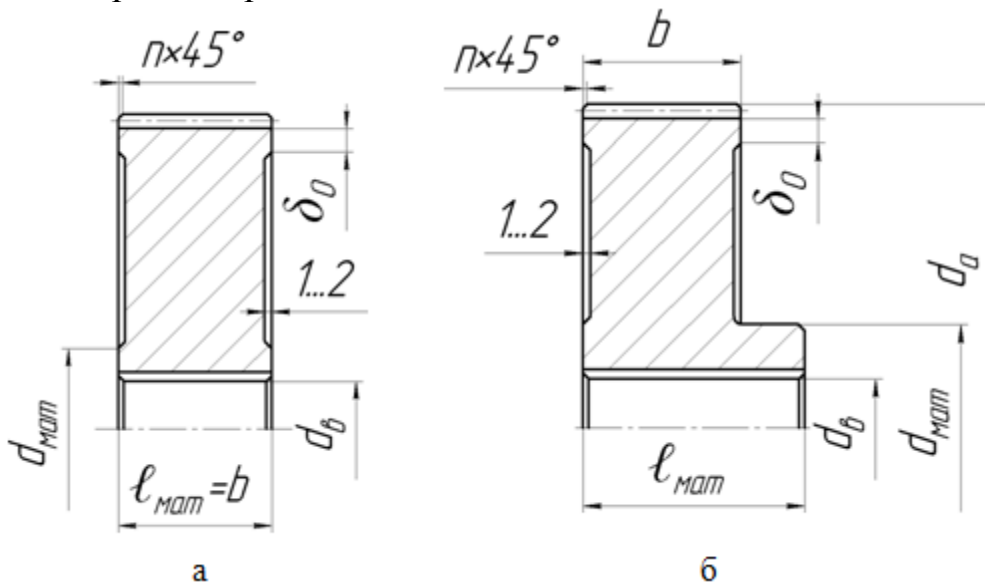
Циліндричні зубчасті колеса з $d_a < 150$ мм
